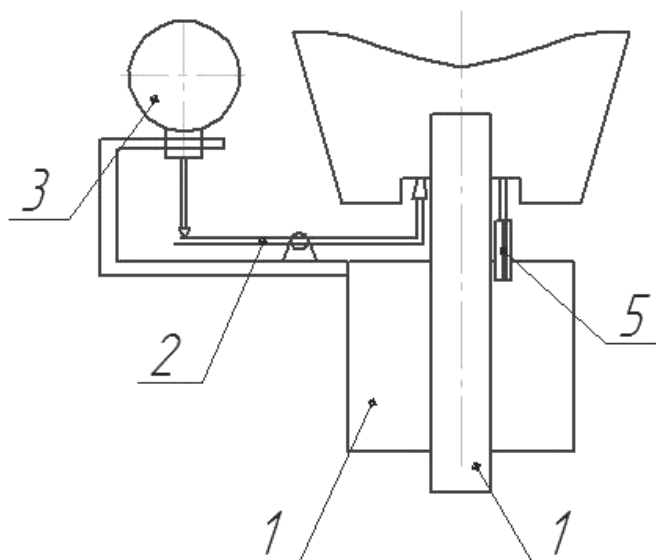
Схема вимірювання: 1 – розтискна оправка, 2 – корпус пристосування, 3 – індикатор, 4 – передаточний механізм, 5 – упор.
